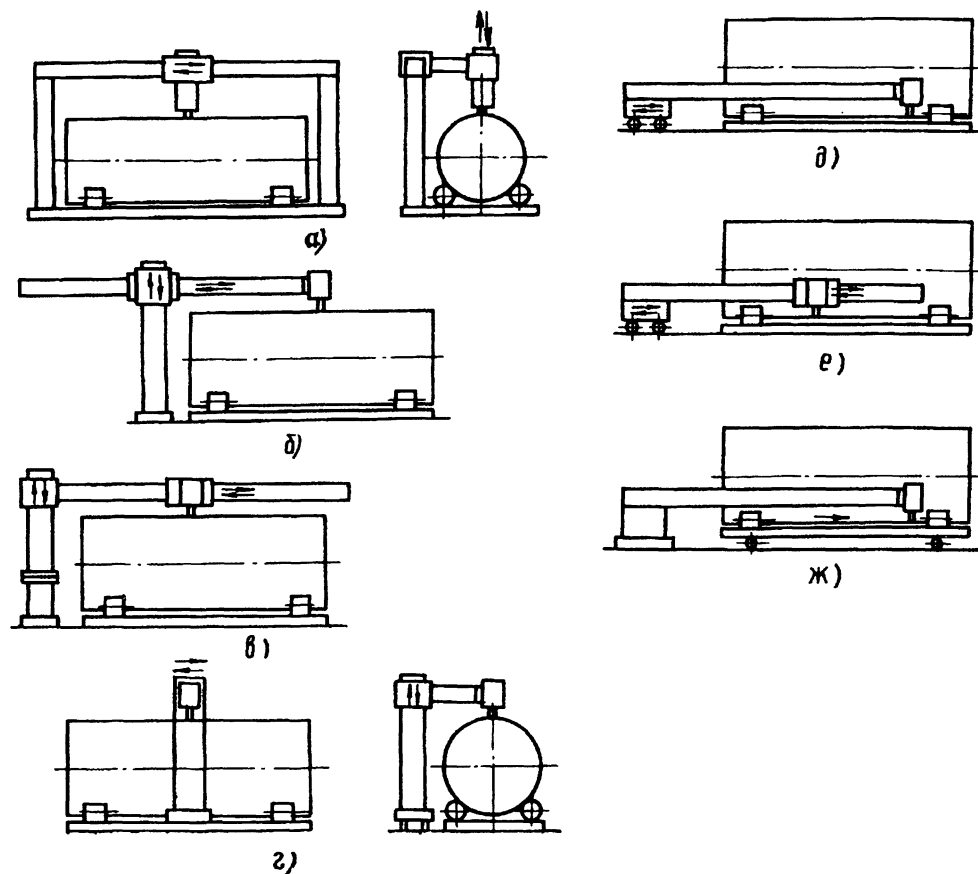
Типовые схемы компоновки установок и станков для дуговой сварки прямых стыковых швов цилиндрических изделий без прижима свариваемых кромок
